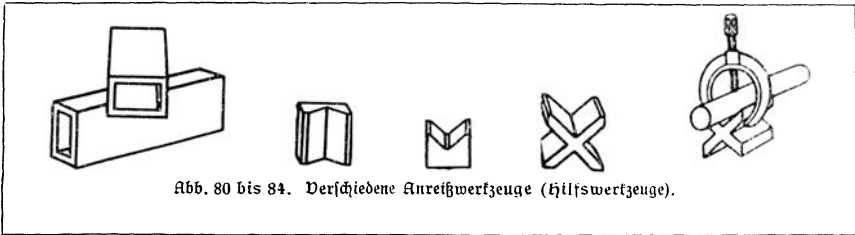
bis 84. Verschiedene Anreißwerkzeuge (Hilfswerkzeuge).
